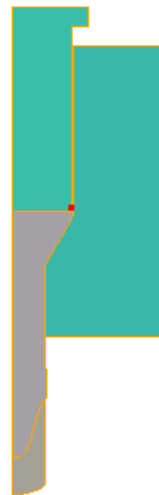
Формоутворення біметалевої заготовки, комбінація Д16-М1
